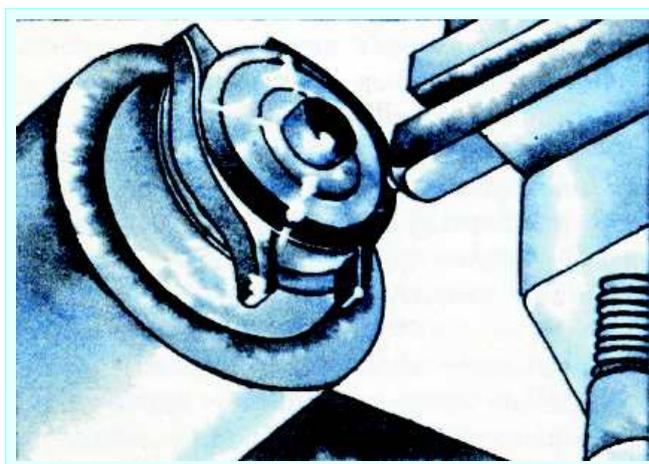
Использование алмазного резца для обтачивания часового корпуса.
